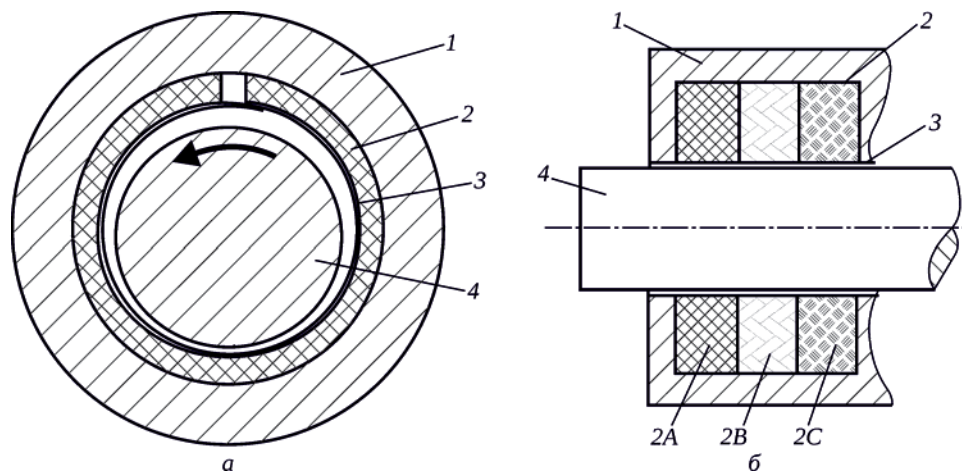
Схема лепесткового подшипника с металлической сеткой [40]:
